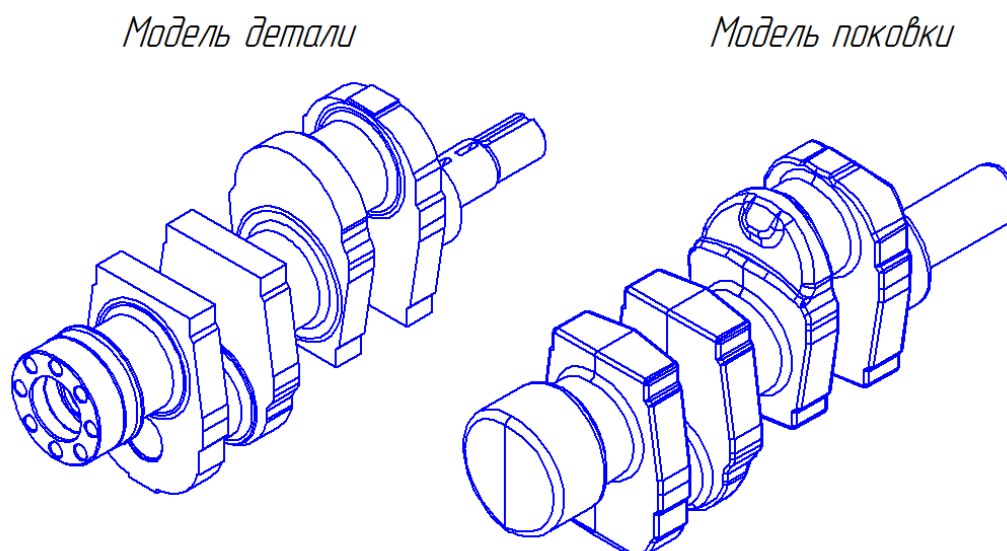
Коленчатый вал Д21-1005015А3, изготавливаемый на АМО ЗИЛ.
